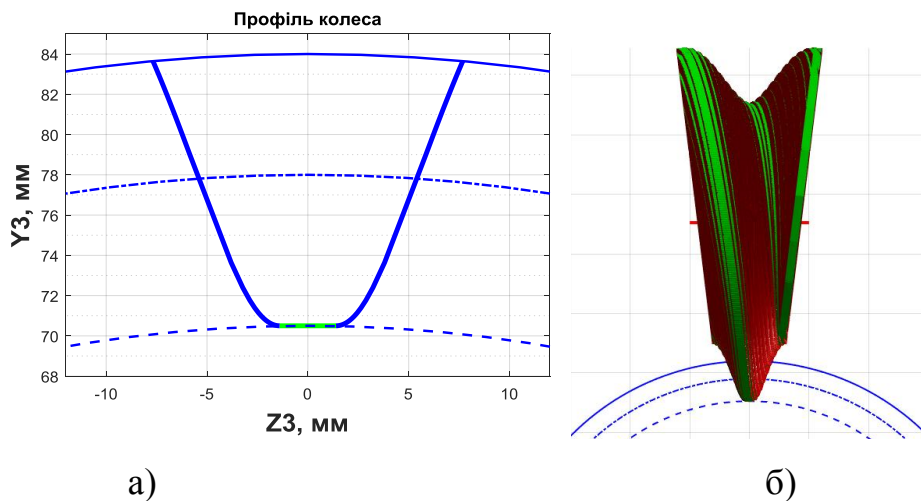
Формоутворення зубчастого колеса дисковим інструментом.
